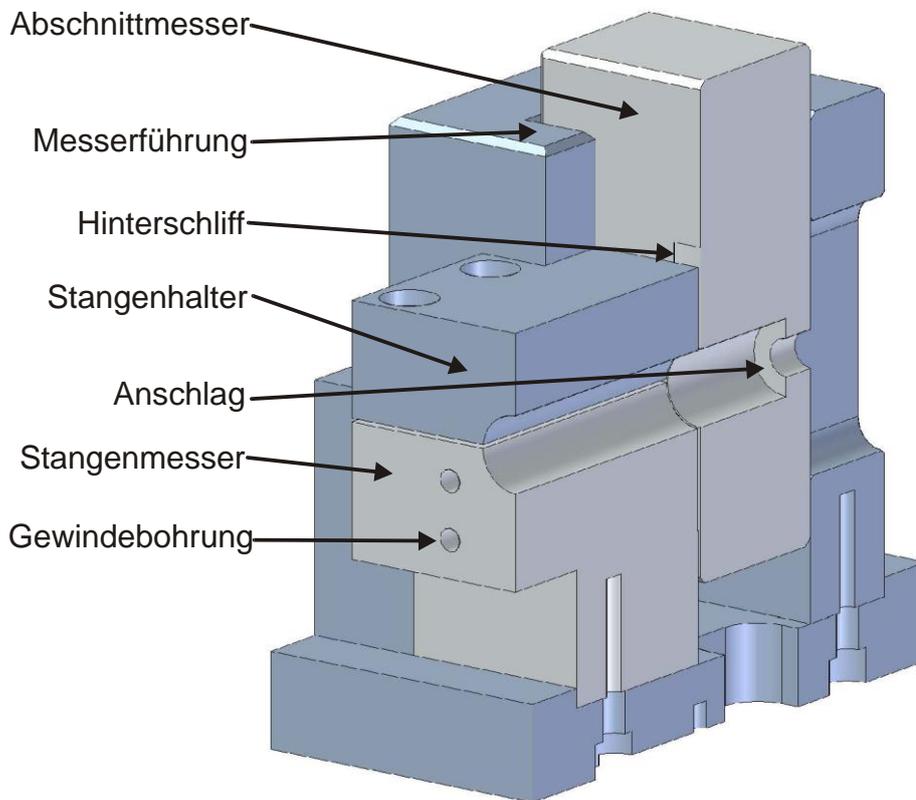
Werkzeug zum Scheren von Aluminiumstangen
